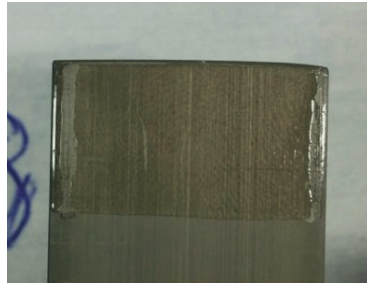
Test de collage sur échantillons de pièces de métal.
